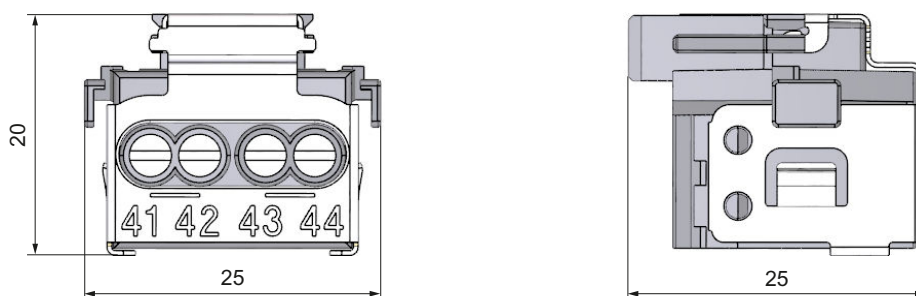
适用于 35 mm 模块的供电元件尺寸图
